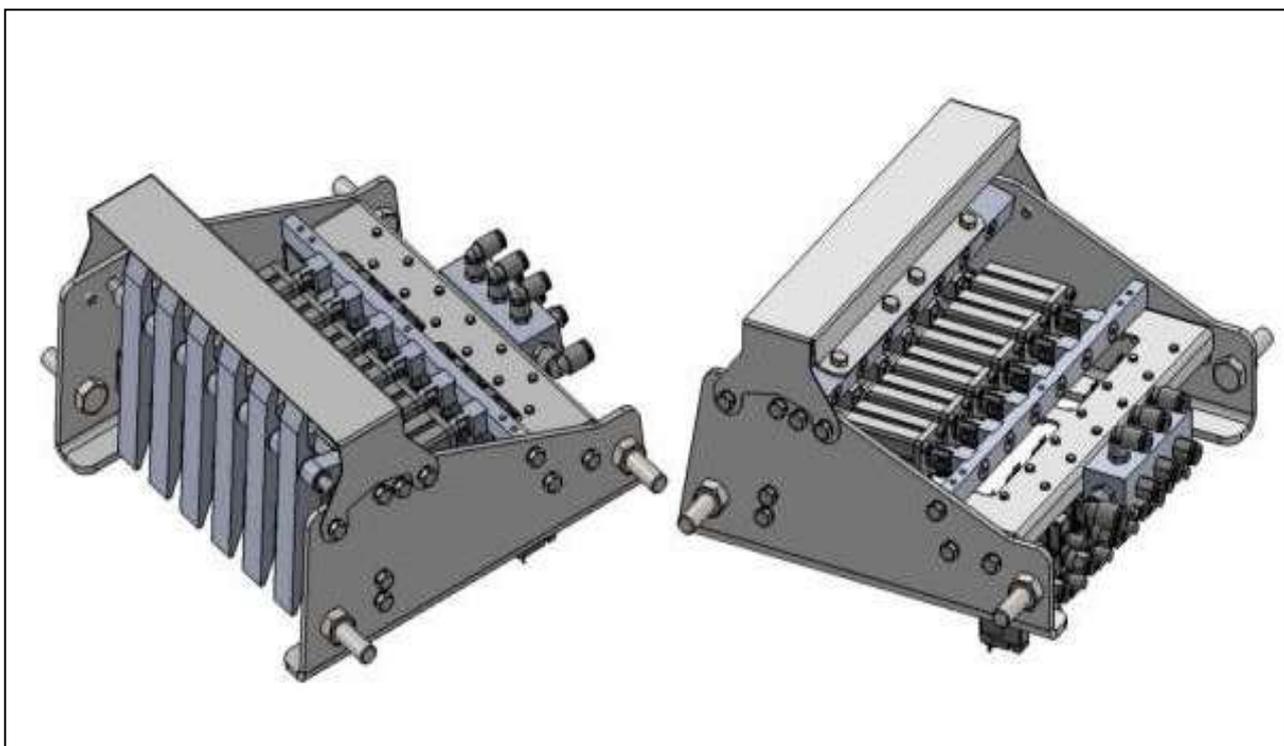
Selezionatore meccanico/pneumatico: modulo per nr. 6 sensori.
